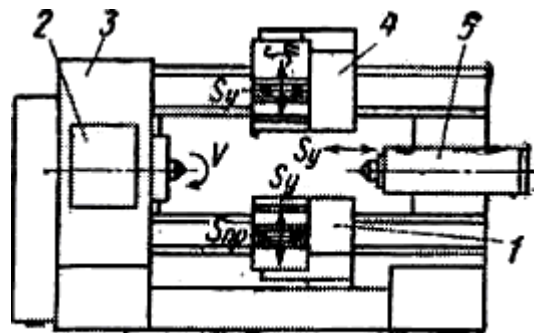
Общий вид многолезцового токарного полуавтомата.
